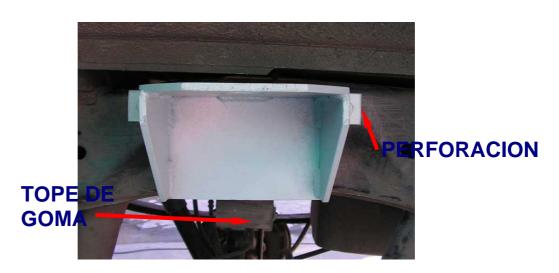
9. Montaje del soporte superior. Vista tren trasero lado izquierdo. Vista frontal
